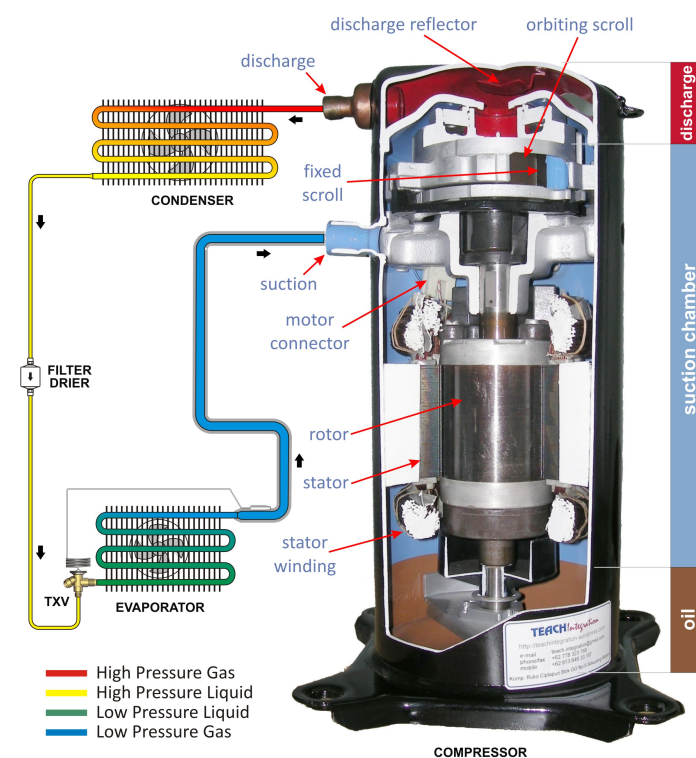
Componentes de compressor hermético tipo “scroll” [33]
